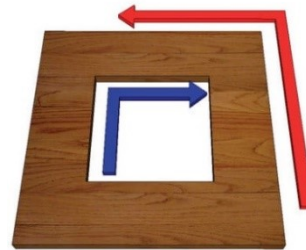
Fräsrichtung für Außen- bzw. Innenkanten
